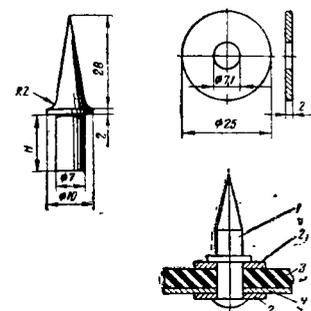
Монтажная схема постановки точеного шипа: 1 — шип; 2 — шайба; 3 — шина; 4 — брезент. Величина H устанавливается по размеру толщины шины.
